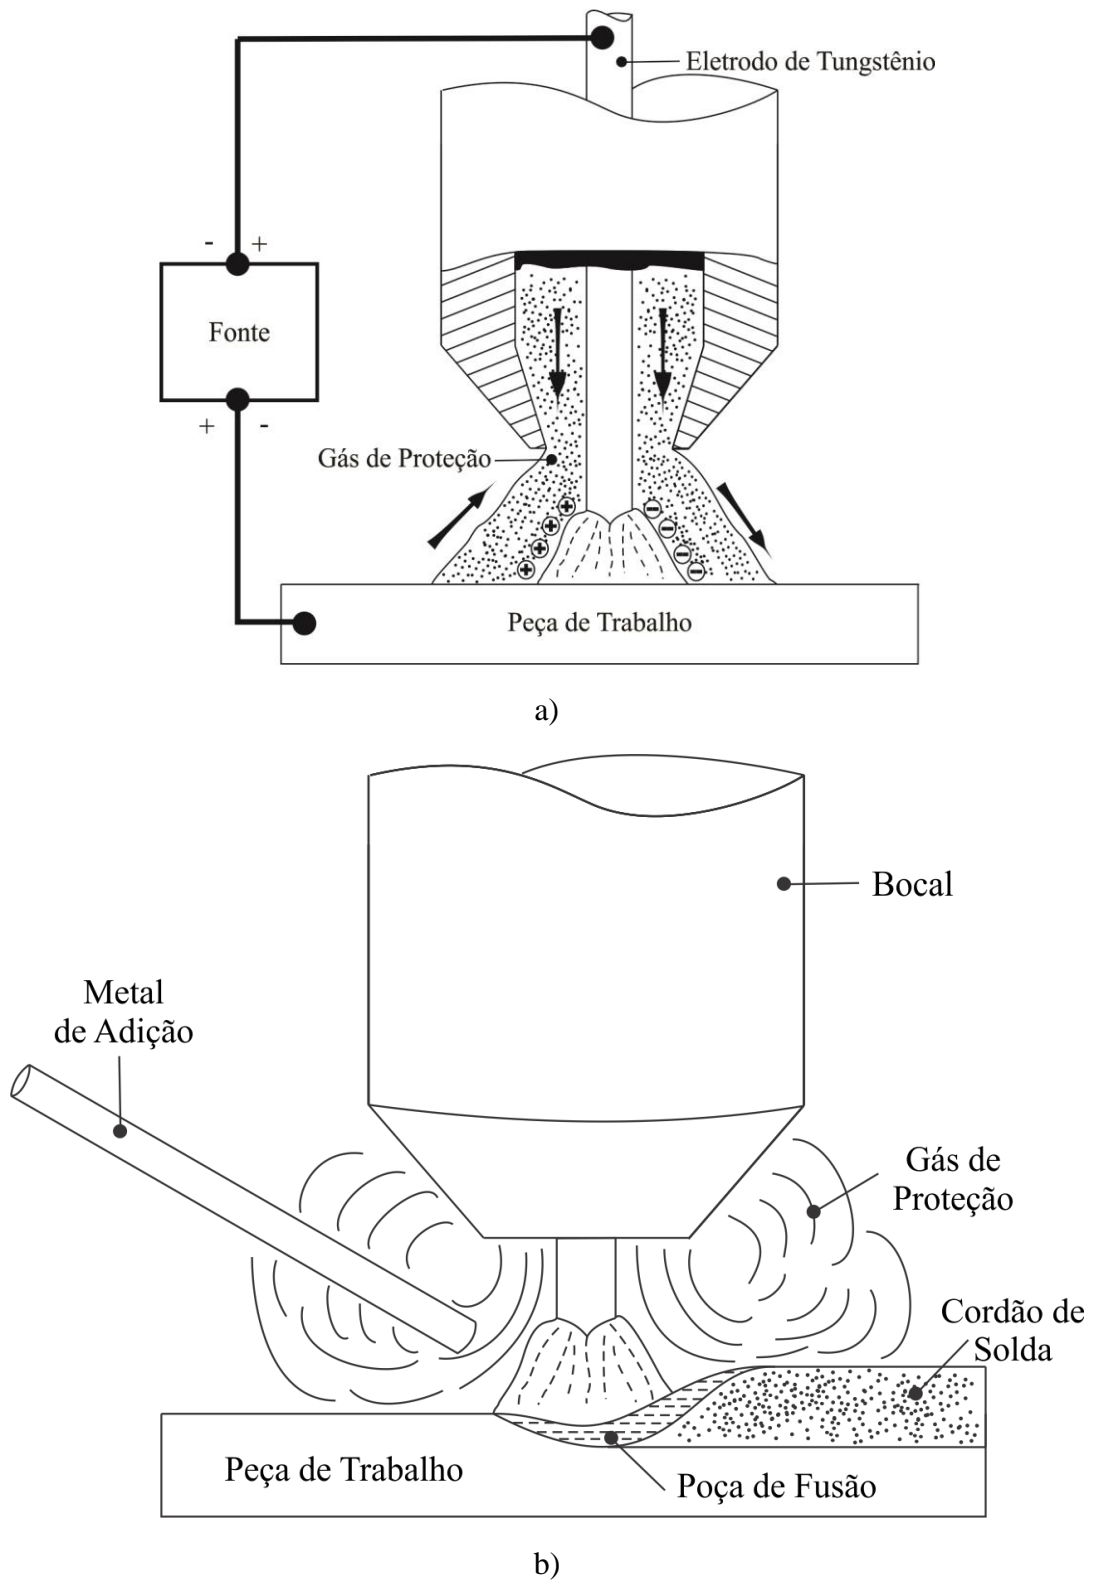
Processo de soldagem TIG: a) Arranjo da tocha e fonte durante o processo; b) Processo TIG em operação, (Adaptado de Lucas, 1990).
